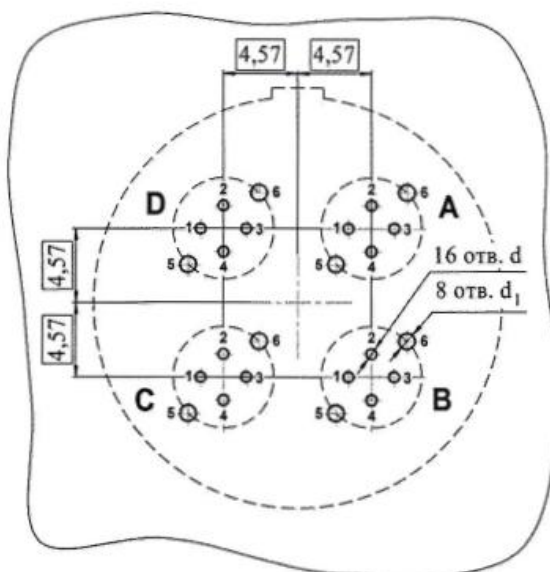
Схема расположения отверстий для установки соединителя
